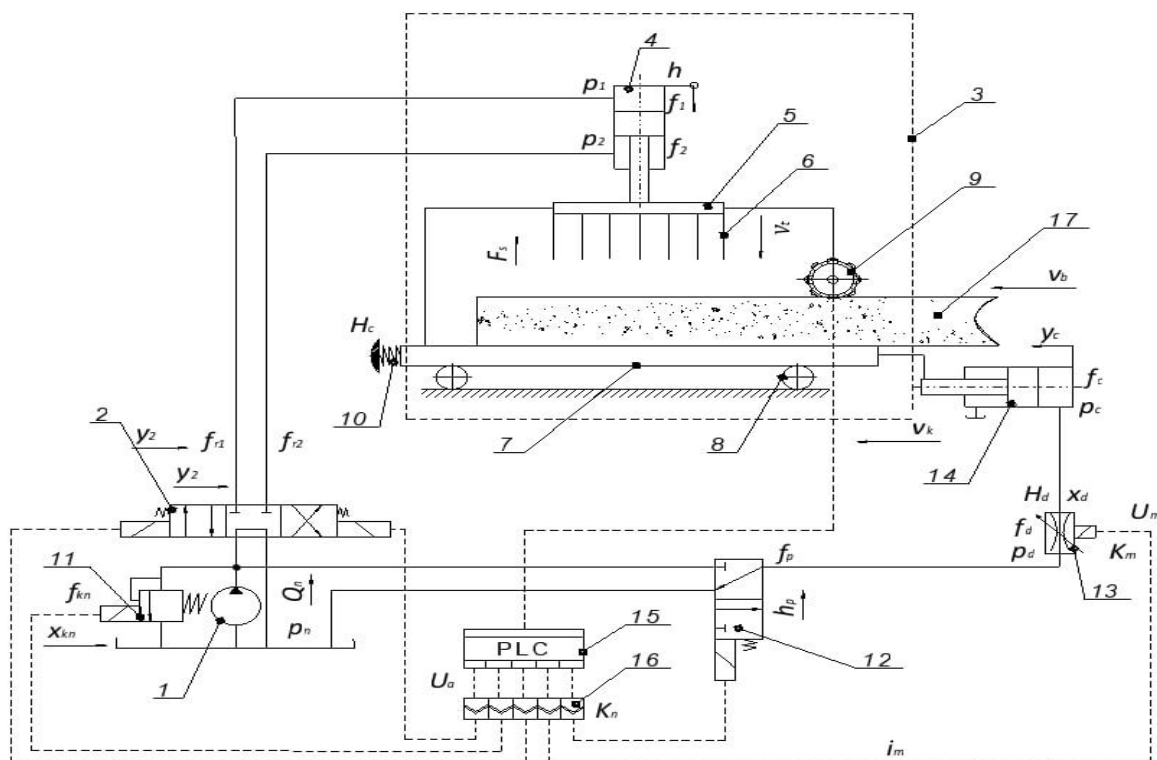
Схема установки для формування заготовки цегли з керуванням від контролера
